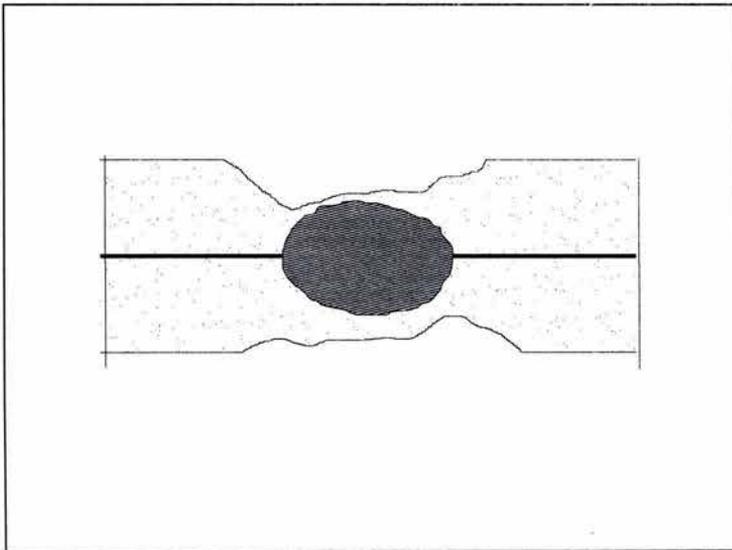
Soldadura incorrecta, mecánicamente débil por pérdida de material.
